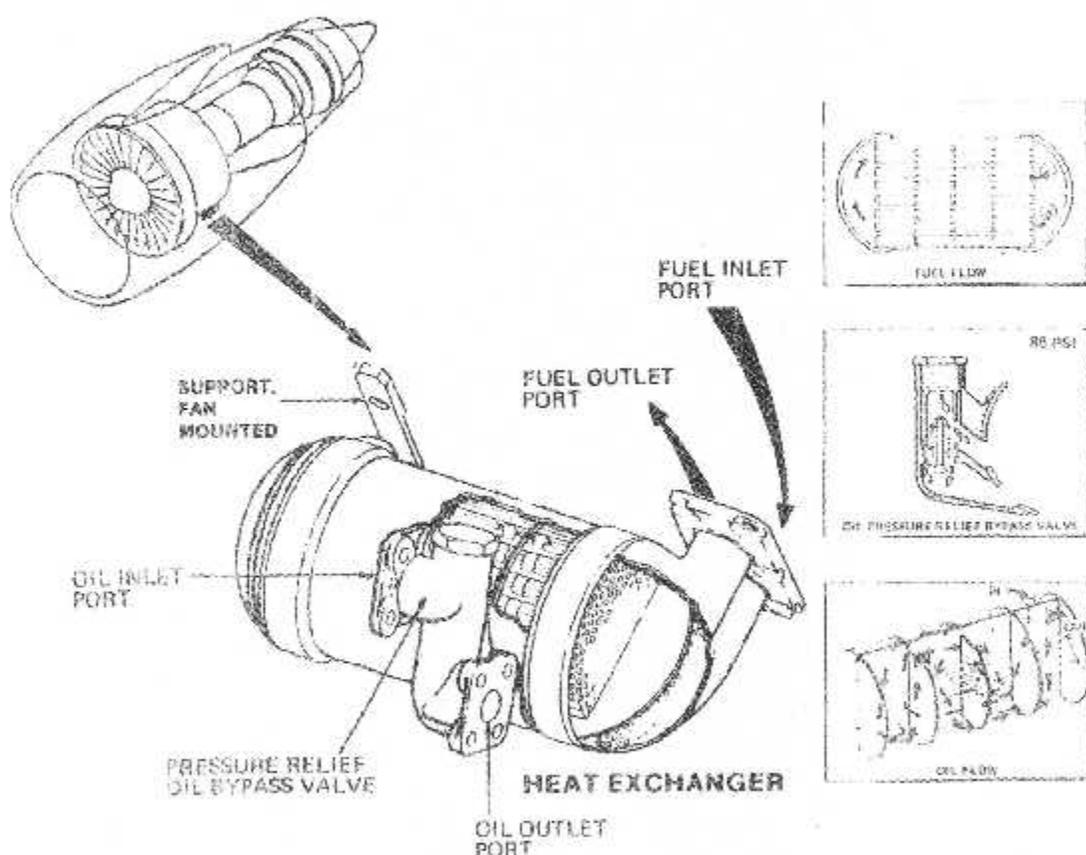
ECHANGEUR THERMIQUE PRINCIPAL CARBURANT/HUILE REACTEUR
